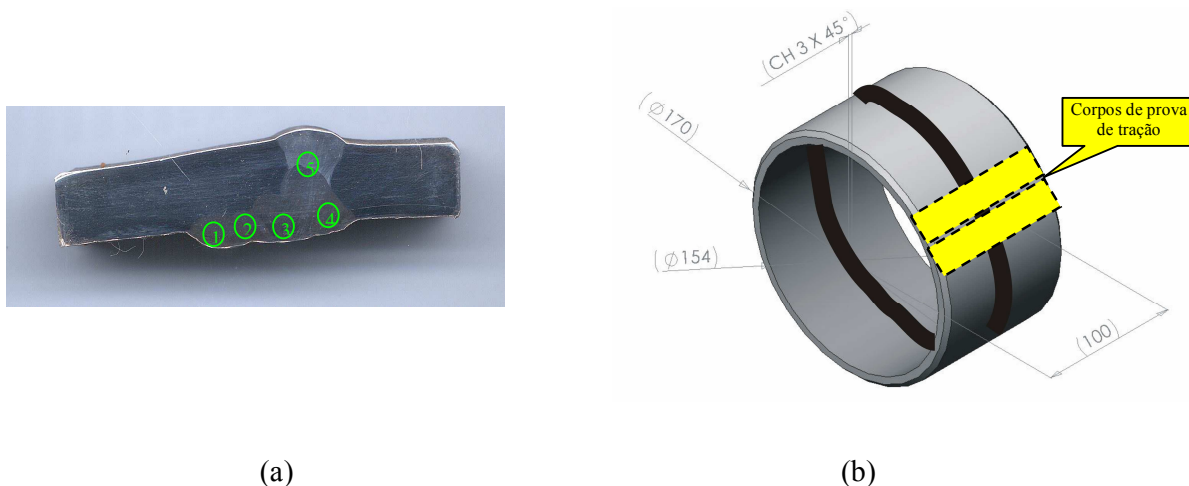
(a) Junta soldada produzida pela Sandvik do Brasil e (b) representação esquemática do tubo de aço inoxidável Superduplex UNS S32750 mostrando a solda transversal à direção de retirada dos copos de prova para os ensaios de tração
